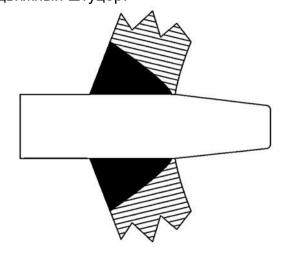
Пример установки гильзы под приварку в стенку трубопровода (Weldin).
